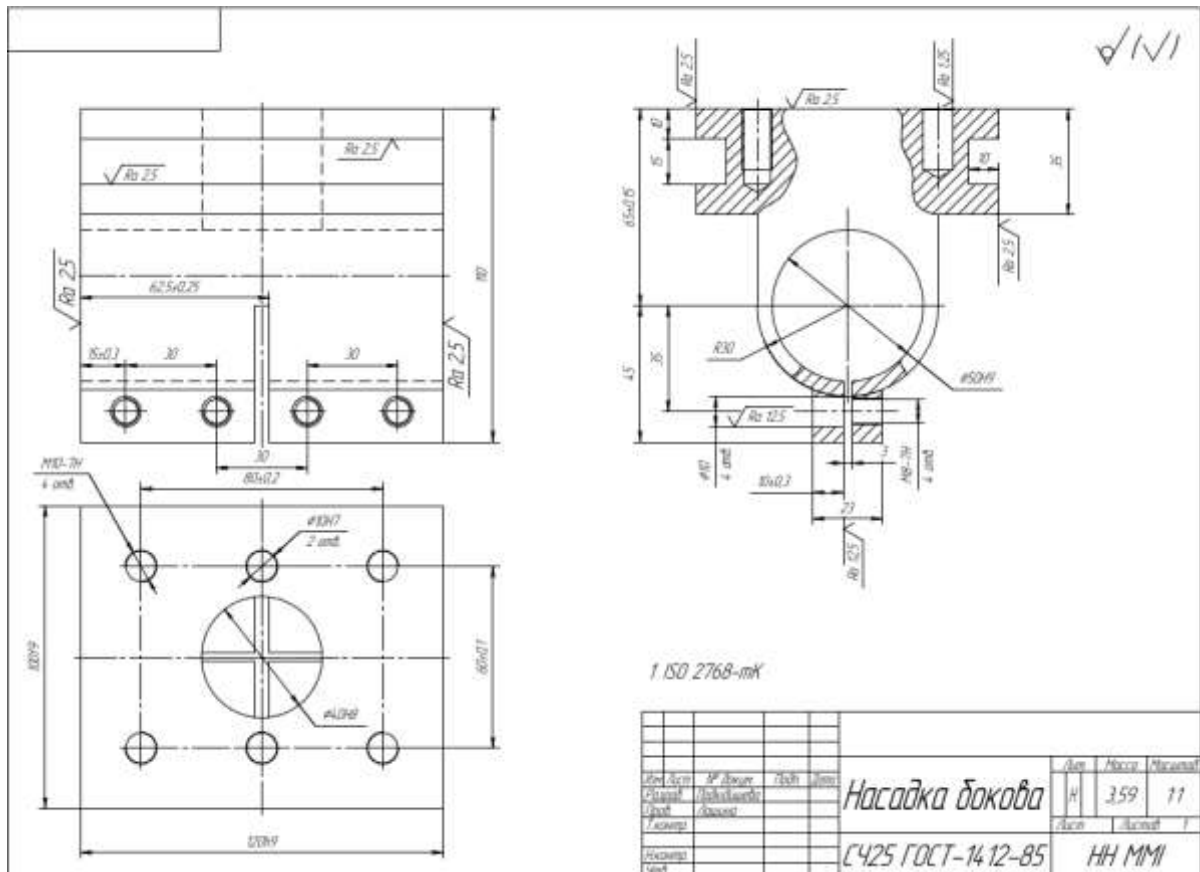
Кресленик деталі «Насадка бокова»
